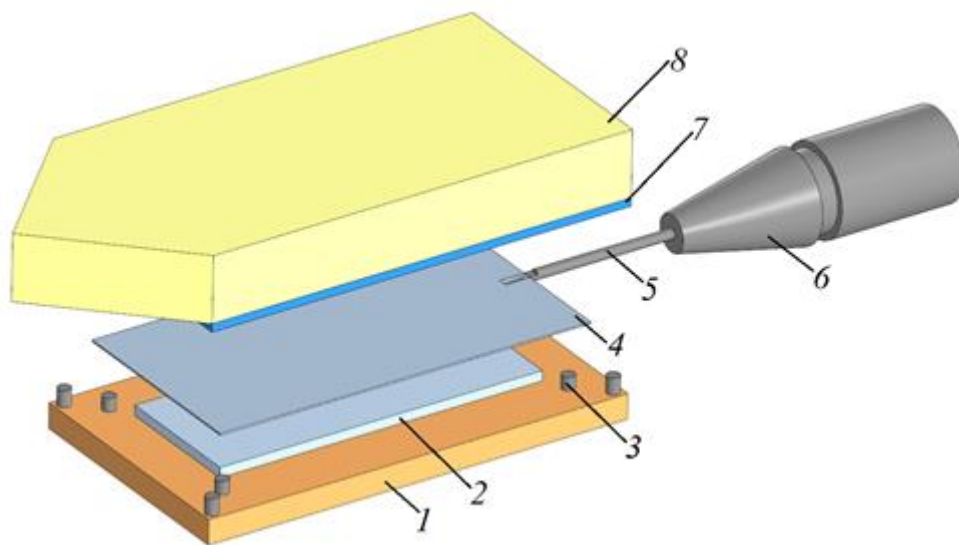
Схема сборки под сварку с воздействием ультразвука: 1 – основание; 2 – неподвижная пластина АМг6; 3 – сварочный зазор; 4 – прослойка; 5 – волновод; 6 – ультразвуковой преобразователь; 7 – метаемая пластина ВТ1-0; 8 – заряд взрывчатого вещества
